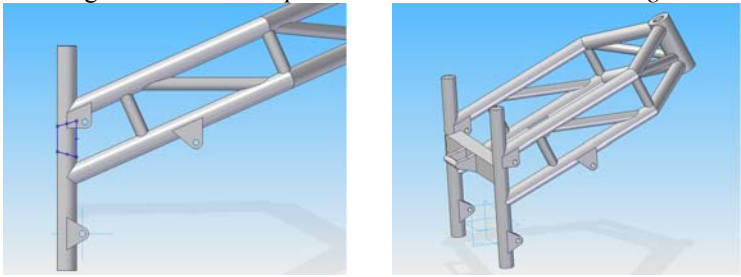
Sezione della barra trasversale e vista del telaio definitivo con tubi tondi pieni.
